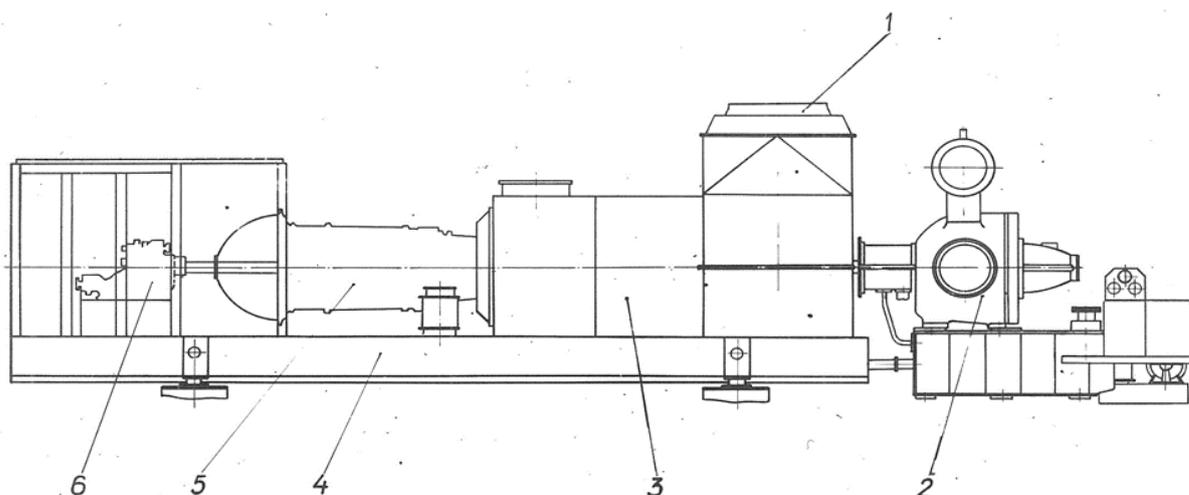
Газоперекачивающий агрегат ГПА-10-01. 1 – Газоотвод, 2 – Нагнетатель, 3 – Кожух, 4 – Рама, 5 – Двигатель, 6 - Блок агрегатов
